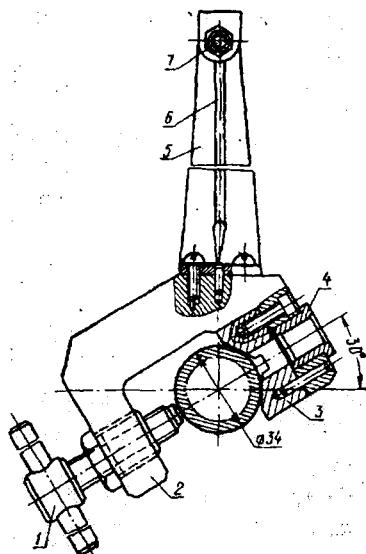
Кондуктор для сверления отверстий под доильные краны:
